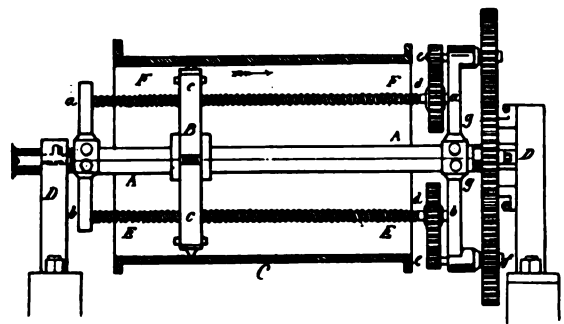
Zylinder-Bohrmaschine mit selbsttätigem Vorschub (Cockerill 1838)
